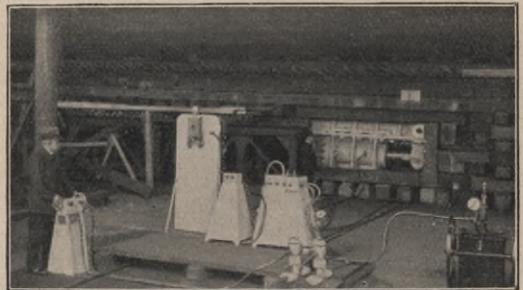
Haltevorrichtung des „Imperator“. (Vulkan-Werke, Hamburg.)
